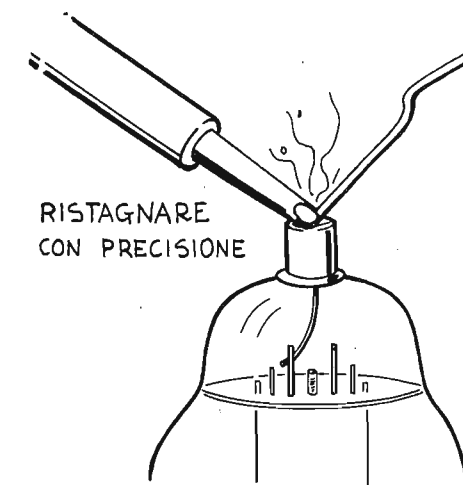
Soltanto quando si è perfettamente certi che il collante ha ultimato la sua opera di adesione delle parti, si ripristina la saldatura a stagno del conduttore di griglia controllo sul cappuccio della valvola.
